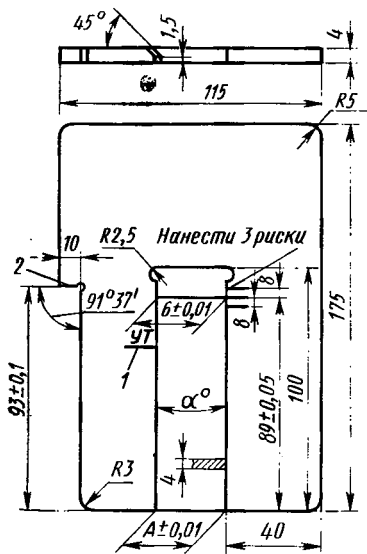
Шаблон для проверки радиального угла хвостов лопаток: 1 — риска утолщенных хвостов; 2 — упор для контроля длины кромки лопатки с упорами 2; 4 — установ; А, Б, К, Л — чертежные размеры, обеспечивающие горизонтальное положение внут-
